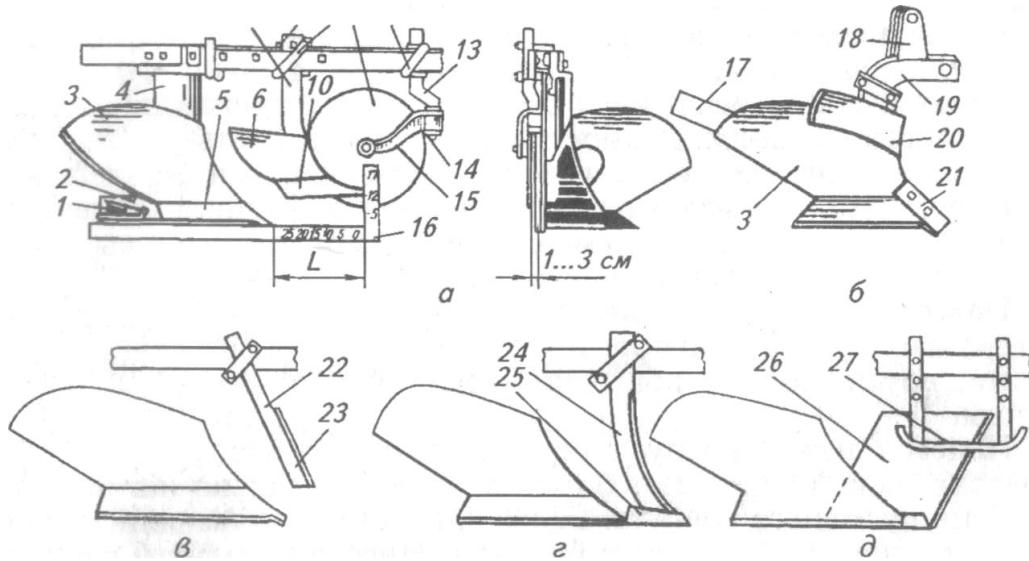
Установка предплужника и дискового ножа (а), углоснима (б), черенкового (в, г) и плоского (д) ножей:
